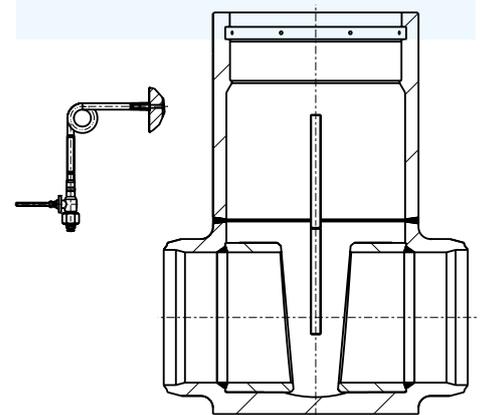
Ausführung mit Bohrung in der Schieberplatte oder Bohrung im Sitzring
